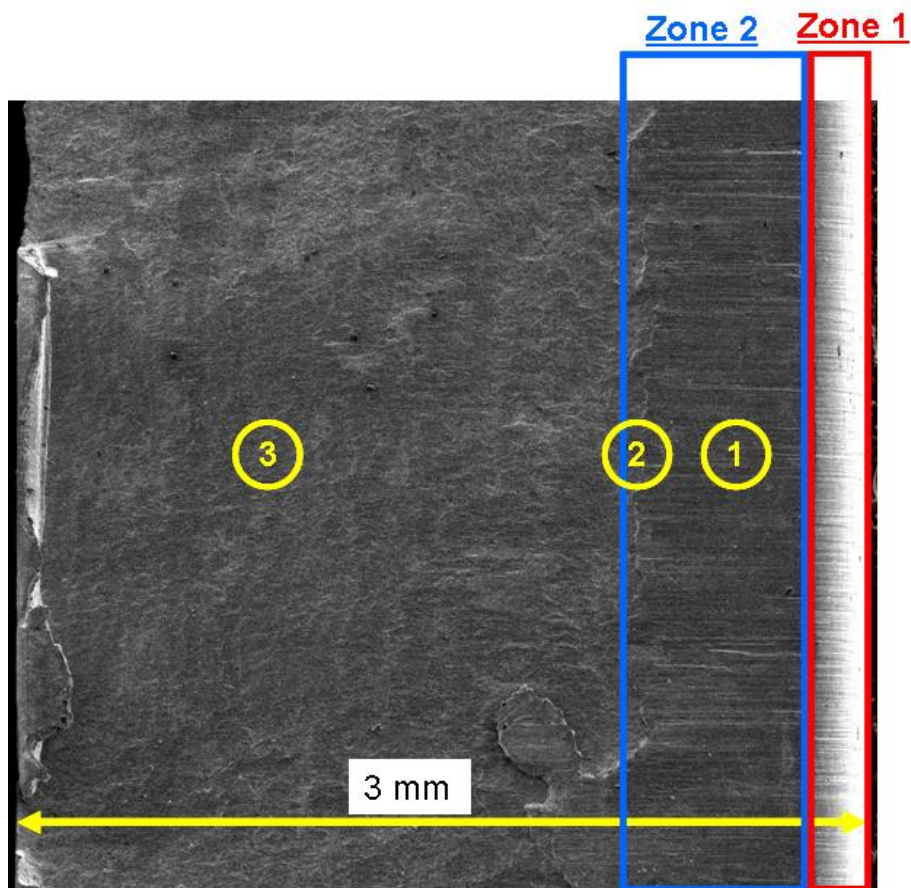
Photo MEB du flan de l'éprouvette
